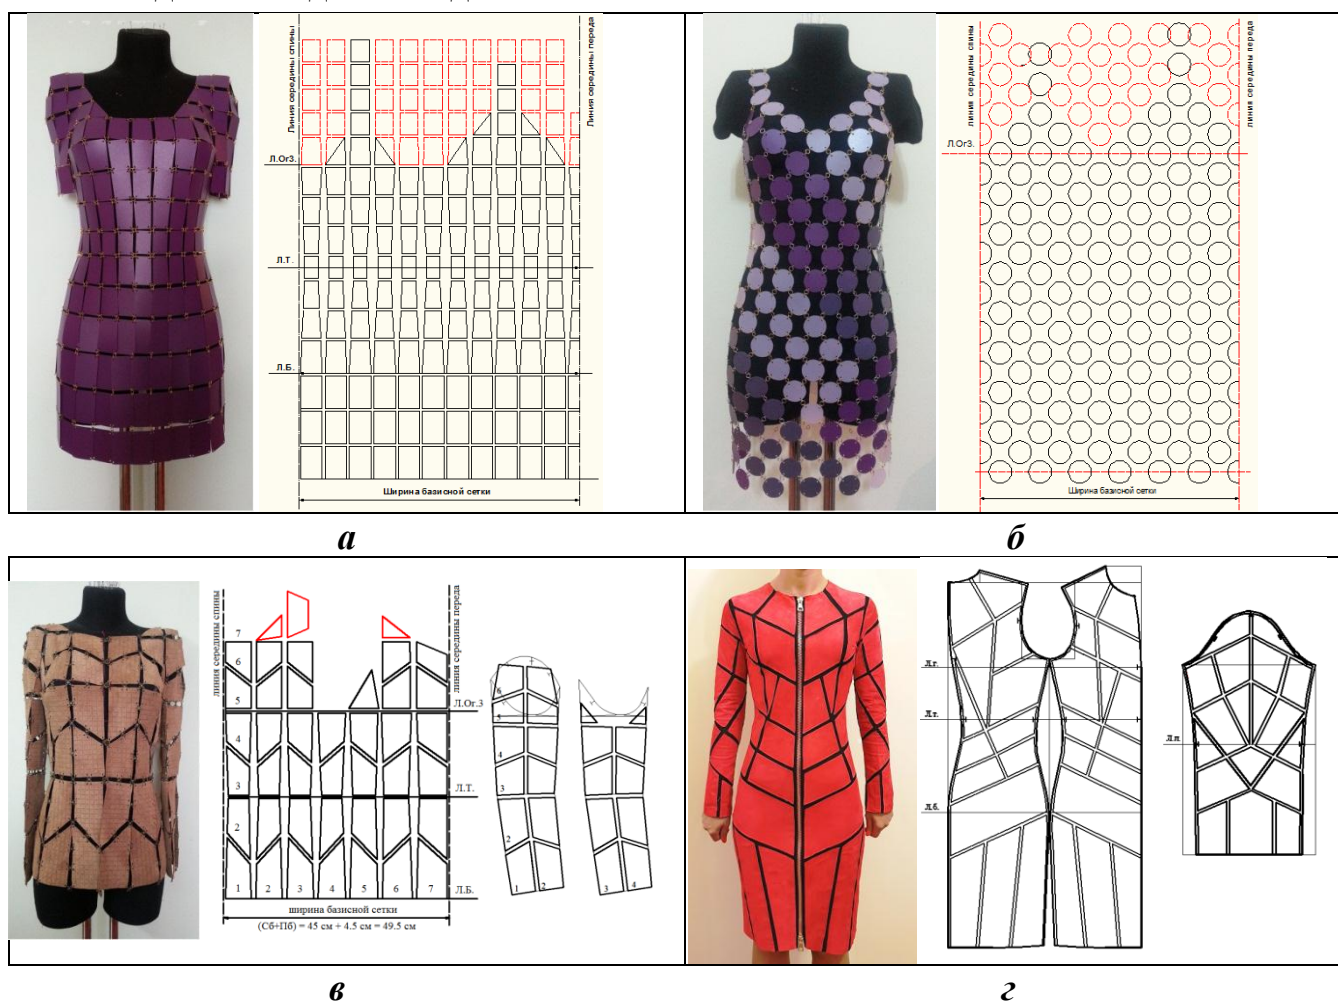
Чертежи конструкций и внешний вид готовых мультидетельных изделий: женских однослойных платьев с неравными деталями кроя (а) и с равными деталями кроя (б), однослойного жакета из замши (в), двухслойного женского платья (г)
